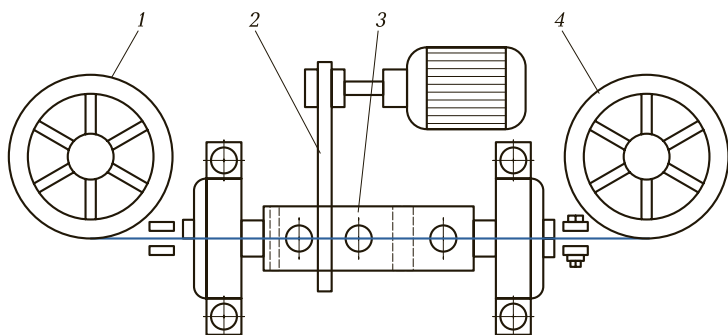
Схема станка для очистки сварочной проволоки:
